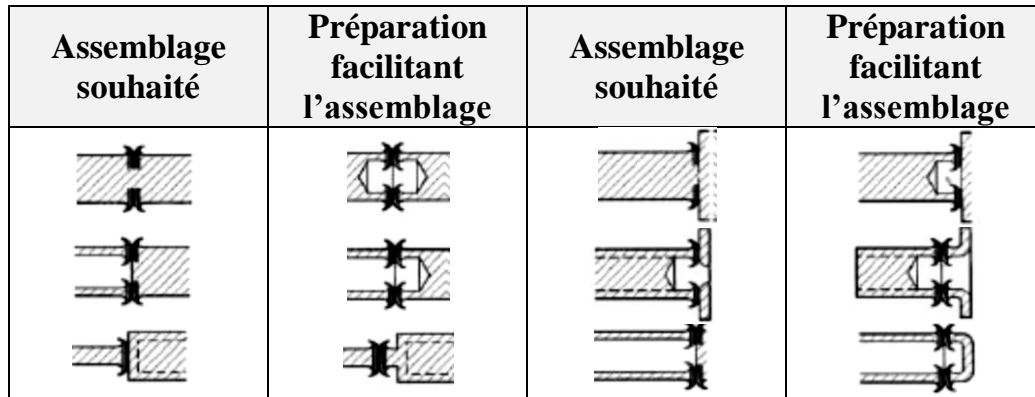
Exemples de préparations de pièces par soudage par friction.
